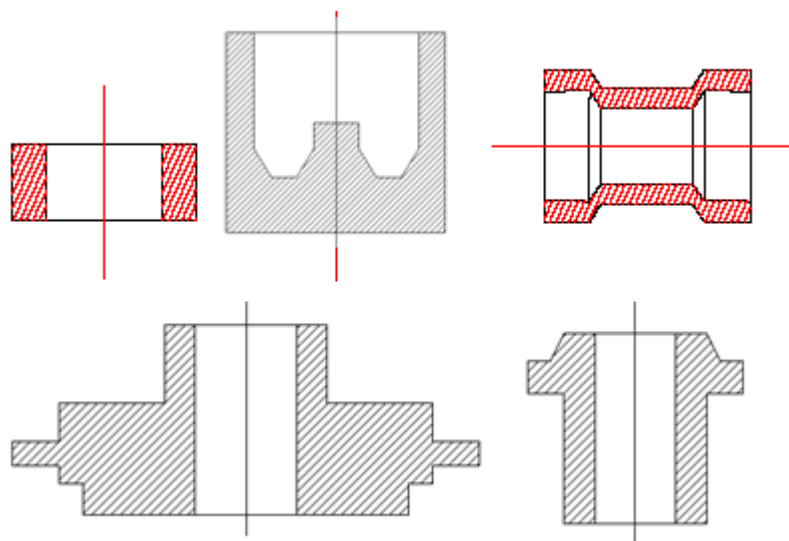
Детали, изготовленные торцовой раскаткой
